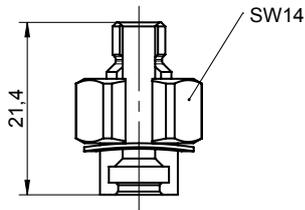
Ausziehvorrichtung, Typ 6419A21B zu Montageadapter Typ 6419A21A
